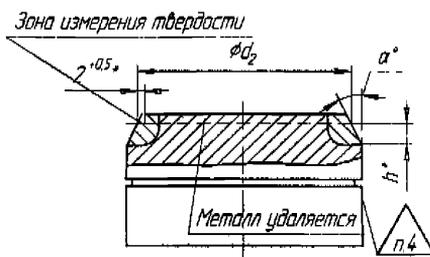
Образец для замера твердости деталей с конусным уплотнением
